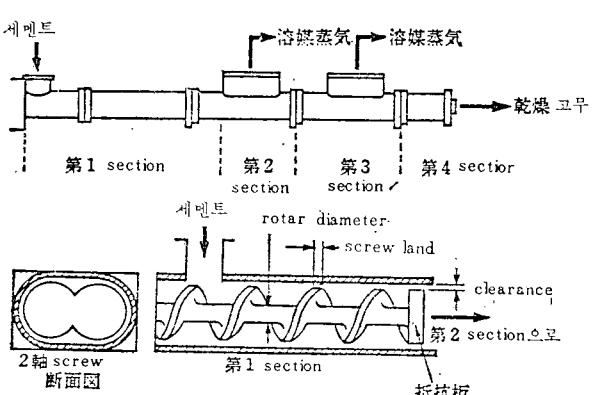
押出機型 乾燥機(Welding Engineer社)
